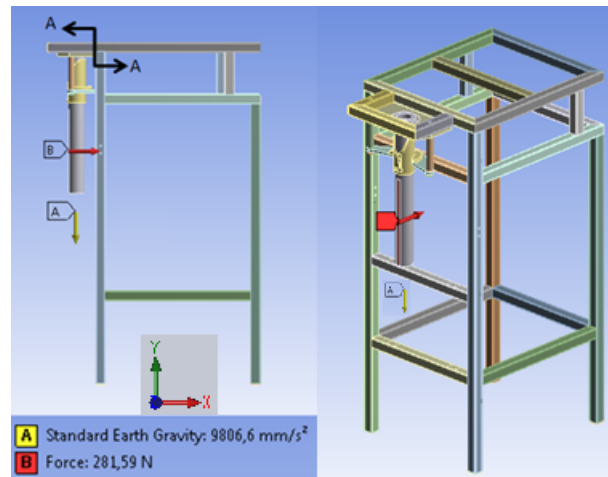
Cargas y sección A-A, de la estructura. Fuente autor
